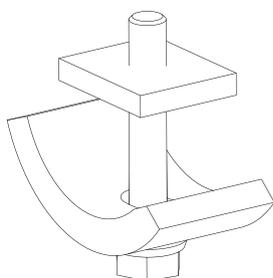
Griffes de serrage, épaisseur de serrage 4-20 mm (acier galvanisé ou V4A)
